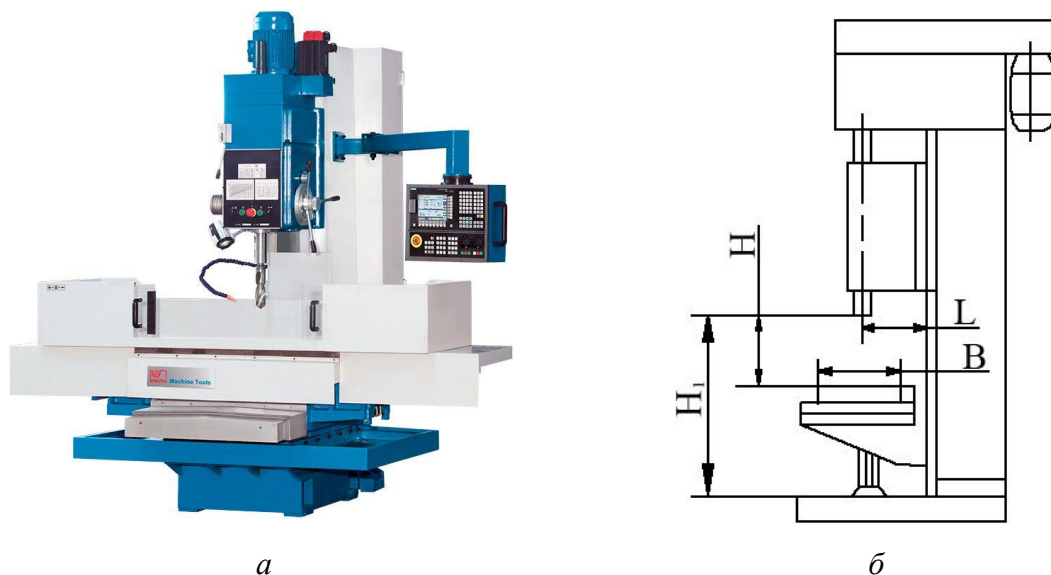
Общий вид вертикально-сверлильного станка с ЧПУ Knuth KSB 40 (а) и схема вертикально-сверлильного станка (б)
